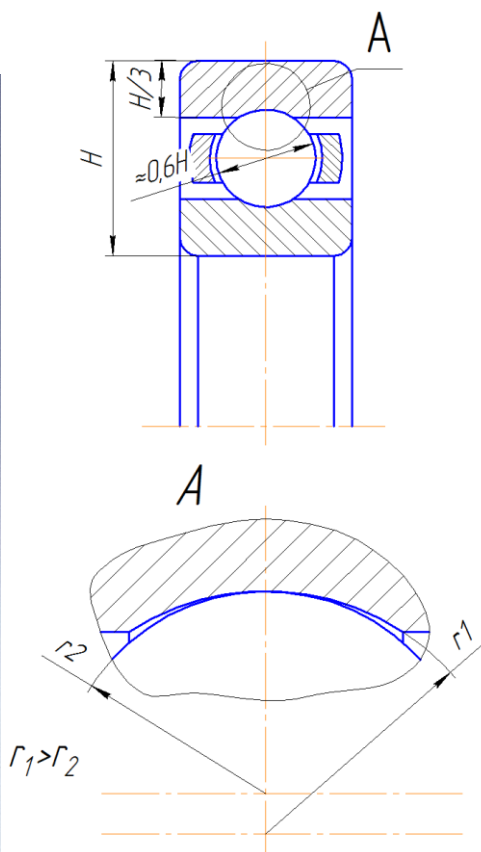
Конструкція кулькового однорядного підшипника.
